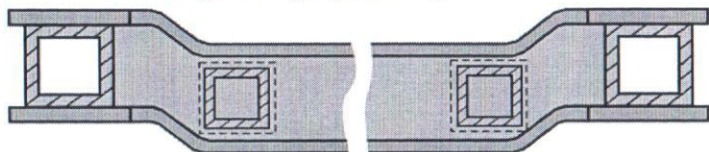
Контроль околошовной зоны сварного соединения приварки средних продольных балок к поперечным
